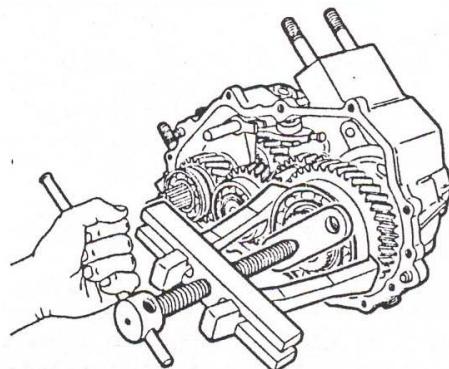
Спрессовка подшипника с шестерней дифференциала
